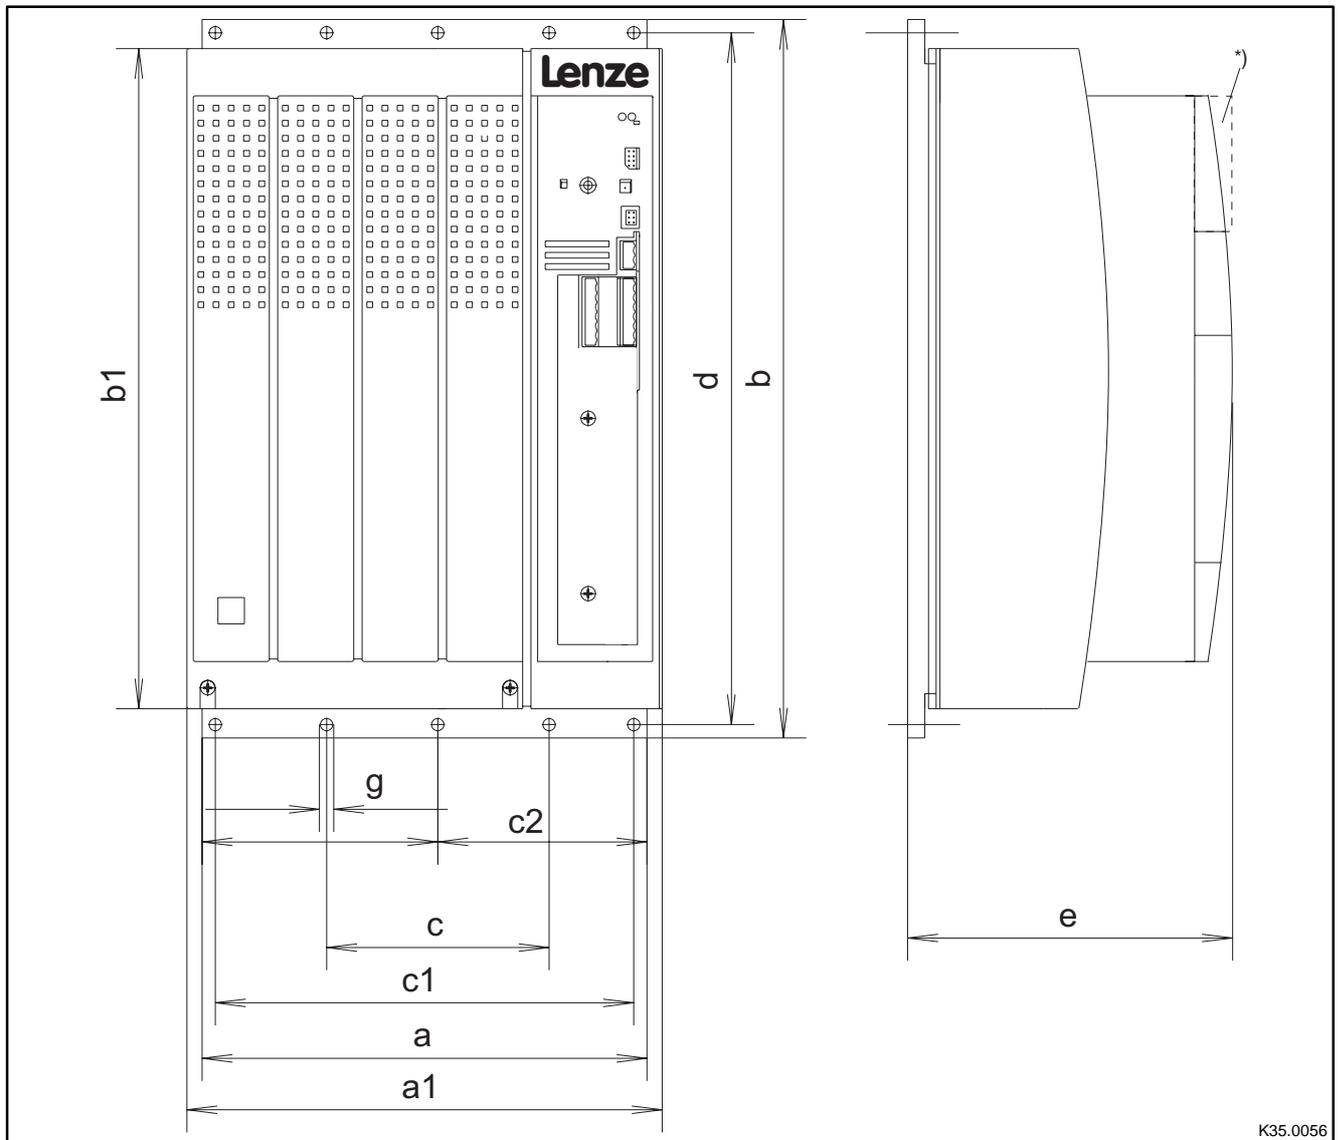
Dimensiones para el montaje según la técnica "Cold Plate"
